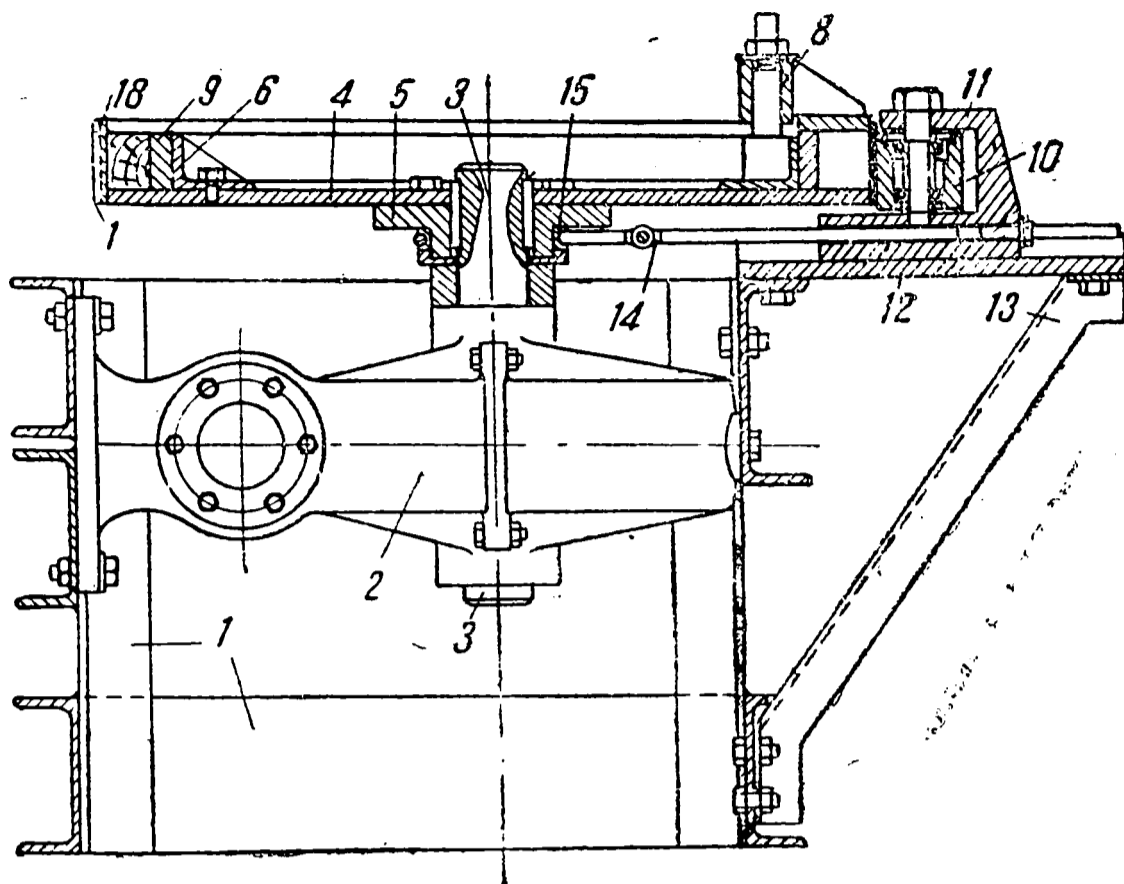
Опытный горизонтальный гнута́рный станок (вид сверху)
